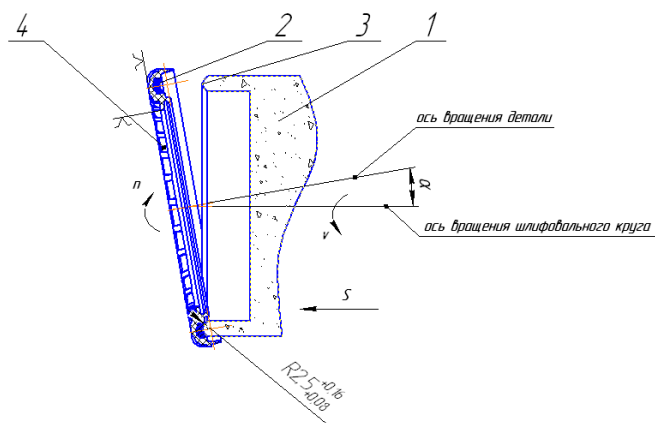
Схема процесса шлифования дорожек качения упорных подшипников
